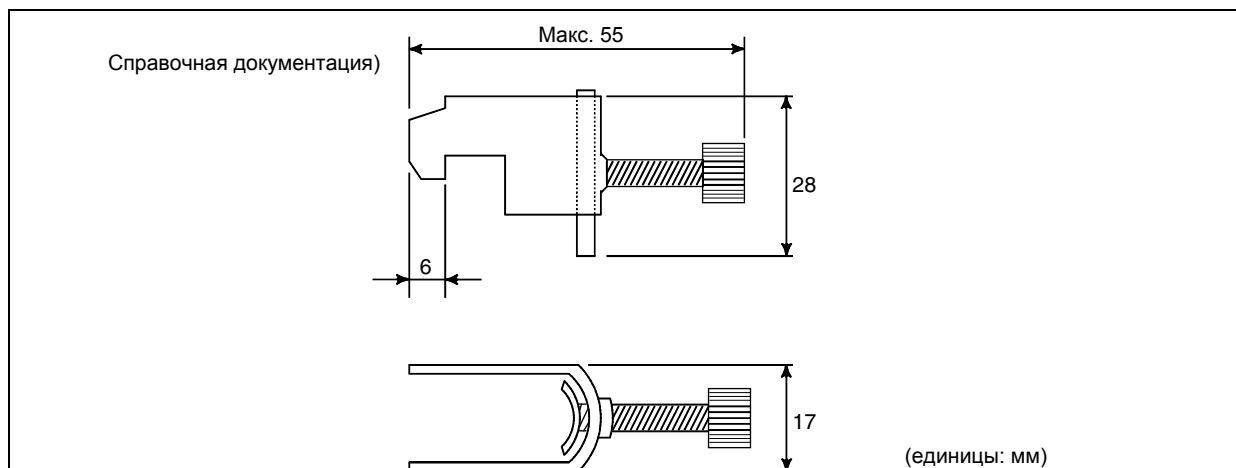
(е) Металлический элемент крепления (схематический чертеж)
